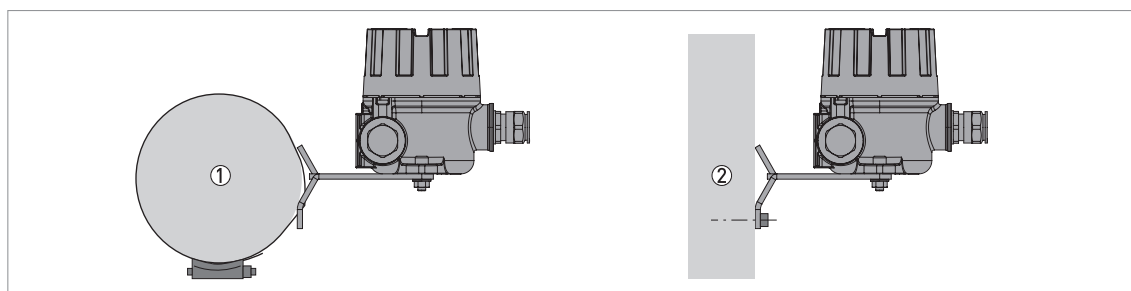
LT40 F: Монтаж корпуса (раздельного исполнения) для модуля электроники: вид сверху
